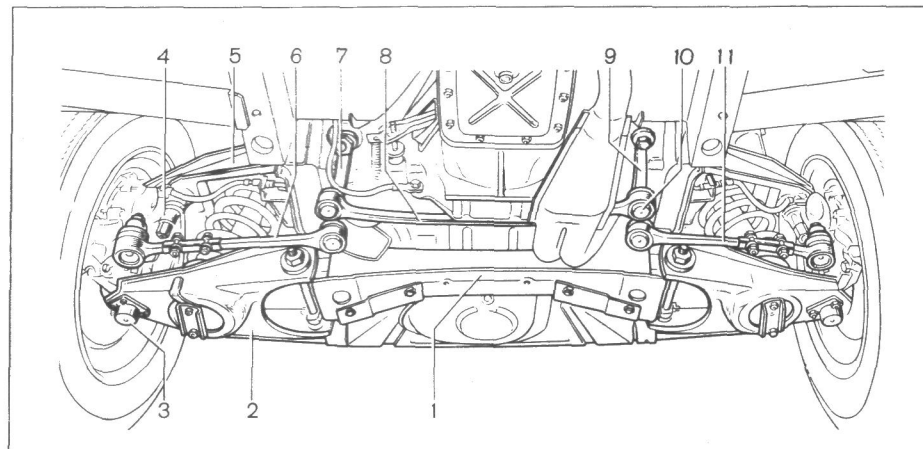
Передняя подвеска и рулевое управление: 1 — поперечина; 2 — нижний рычаг; 3 — шаровая опора нижнего рычага; 4 — шаровая опора верхнего рычага; 5 — верхний рычаг; 6 — левая боковая рулевая тяга; 7 — сошка; 8 — средняя рулевая тяга; 9 — маятниковый рычаг; 10 — шаровой шарнир; 11 — правая боковая рулевая тяга
